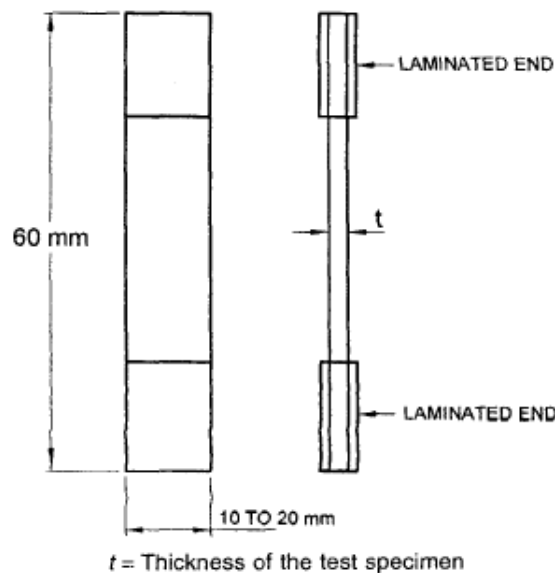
Dimensões do corpo de prova para teste a tração. Fonte: IS 6874 (2008).
